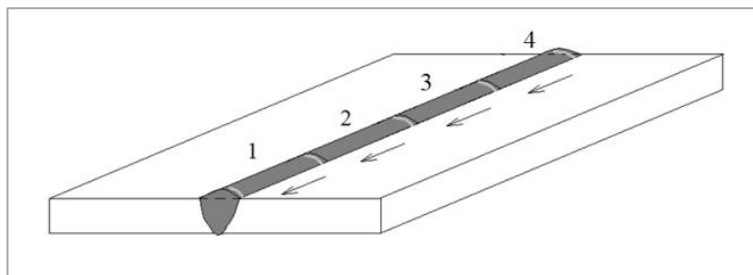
Passes de soldadura com sequência alternada - [10] Imagem adaptada
